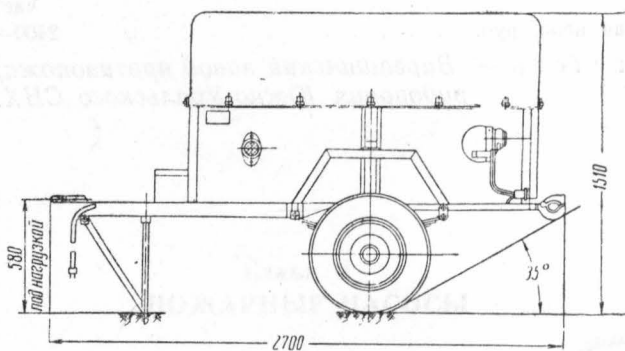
Автомобильный рукавный прицеп РП-0,8
